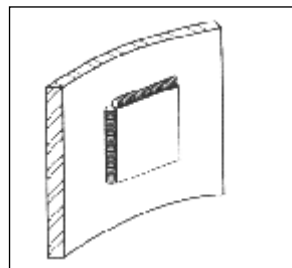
Planchuela de refuerzo, sellada por soldadura - la mejor resistencia a la corrosión
